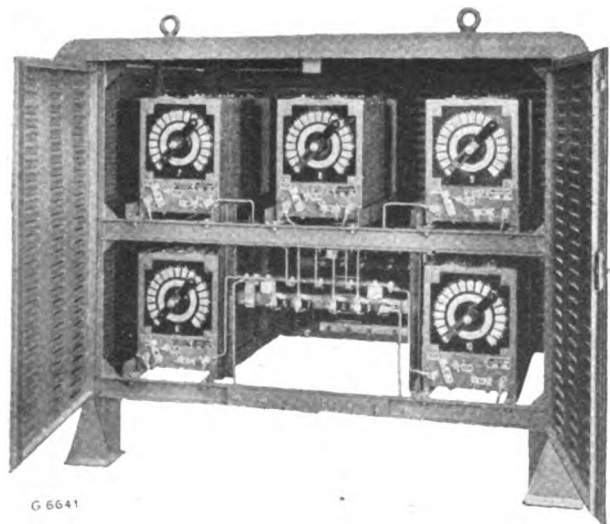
Ansicht eines Schweißstromreglerschranks für eine Vielstellenschweißanlage für 10 induktive Schweißstromregler.
